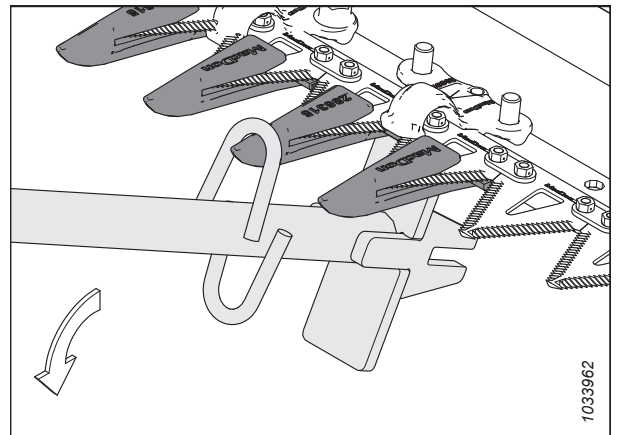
Регулировка смещением вниз — заостренный противорежущий палец
